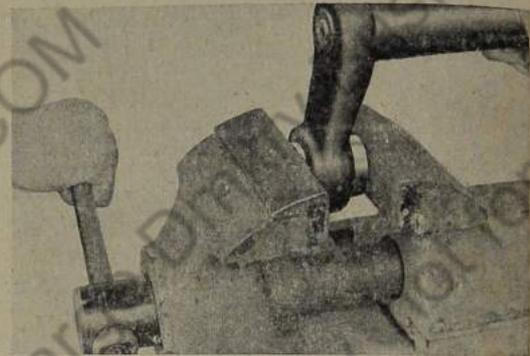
Äußeren Laufring des Kegelrollenlagers einpressen
